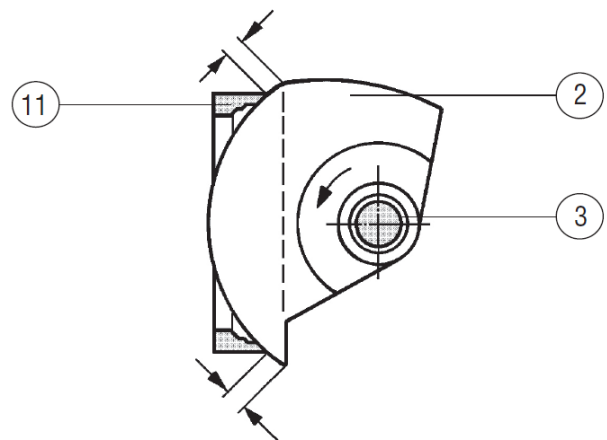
Центровка сферической части шарового сектора при регулировке привода
